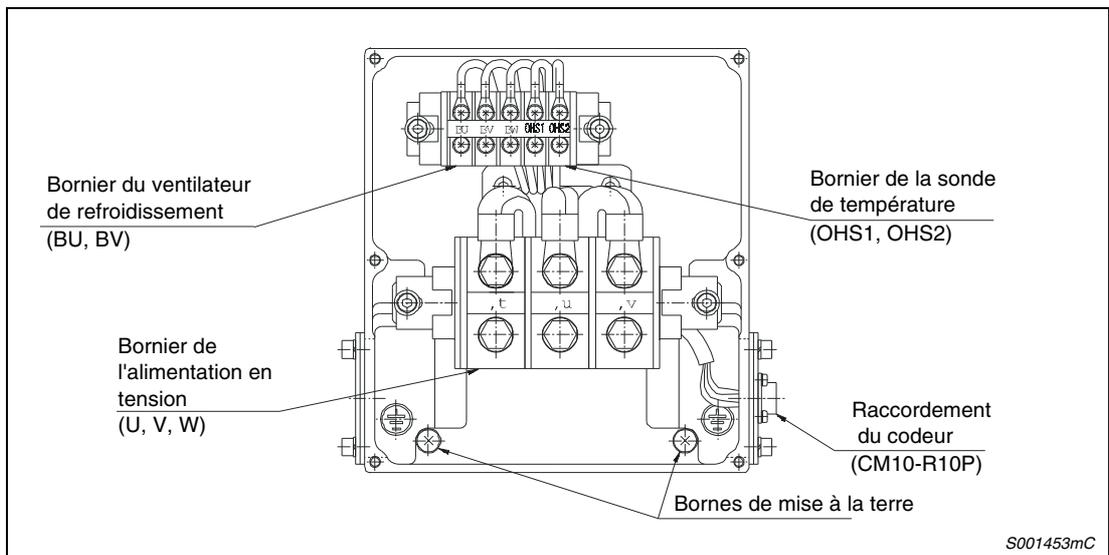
Bornier des moteurs HA-LP15K2(4)(B) et HA-LP22K2(4)(B)
